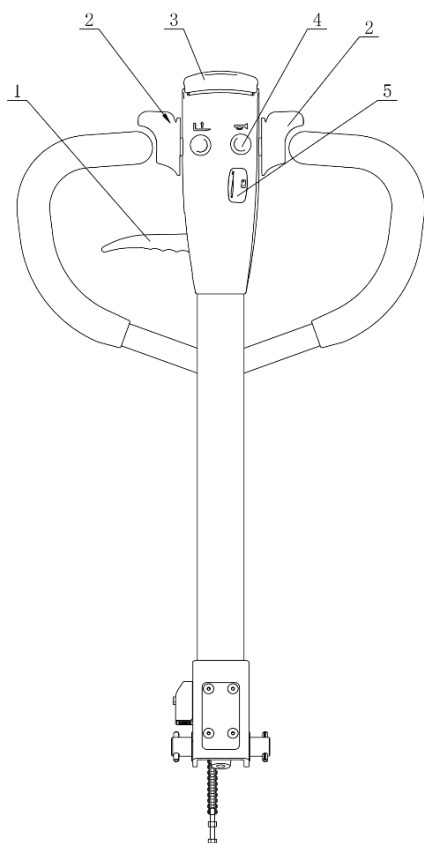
Установка корпуса рукоятки на гидравлический узел
